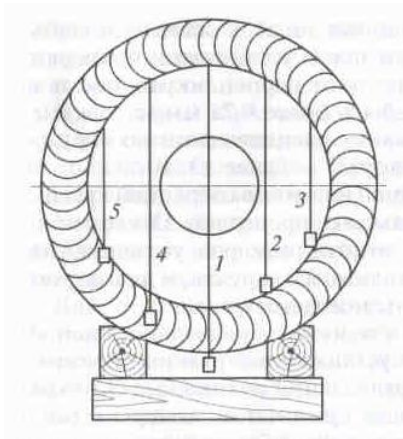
Проверка торцевого и радиального биения крыльчатки
